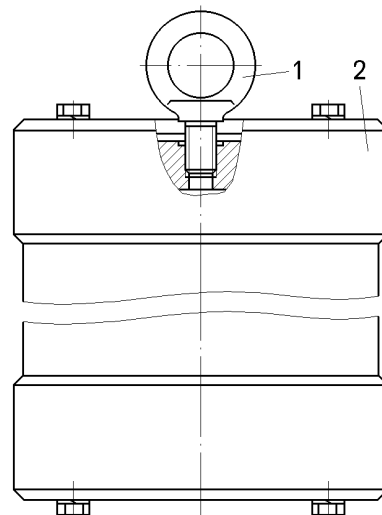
Схема зачаливания для снятия и установки пневмогидроаккумулятора:
